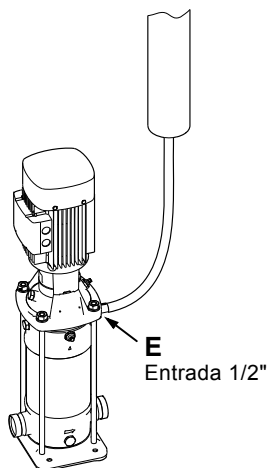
Cierre en tándem con suministro de líquido de enjuague
